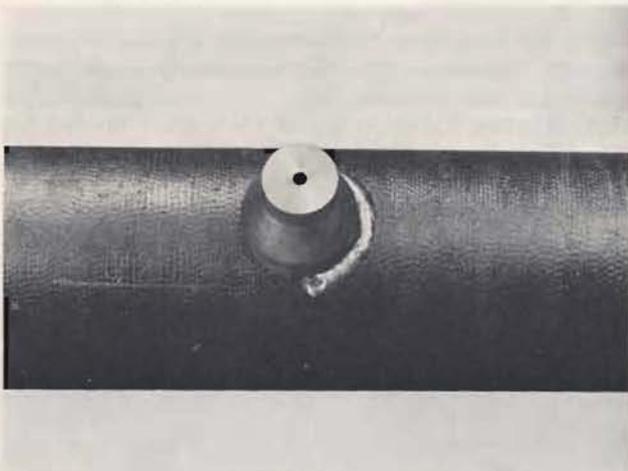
Kupferdorn beim Schweißen der Puffernaht
